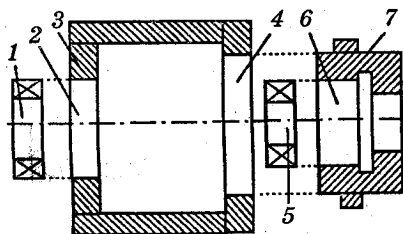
Схема восстановления неподвижных сопряжений: 1, 5 — подшипники качения; 2, 4, 6 — посадочные отверстия; 3 — корпусная деталь; 7 — стакан подшипника
